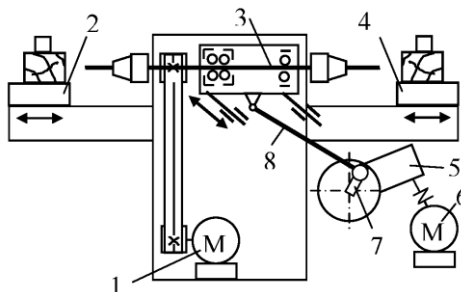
Схема горизонтального двостороннього свердлильно-фрезерного верстата
